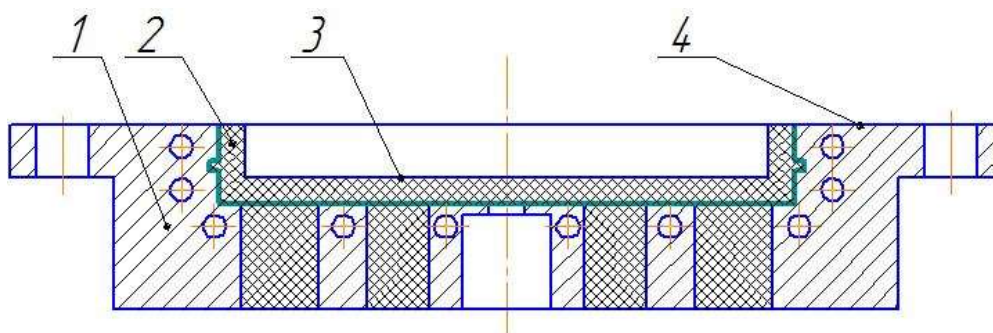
Схема комбинированной металл-металлополимерной формообразующей детали пресс-формы.
